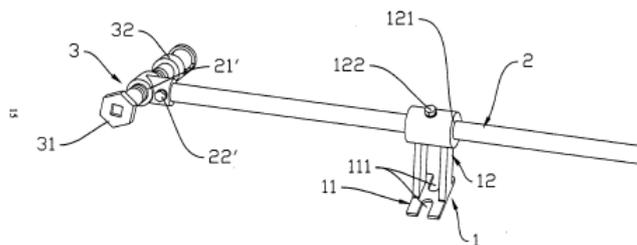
TWM 420395 - Disassembling tool for engine valve spring.
